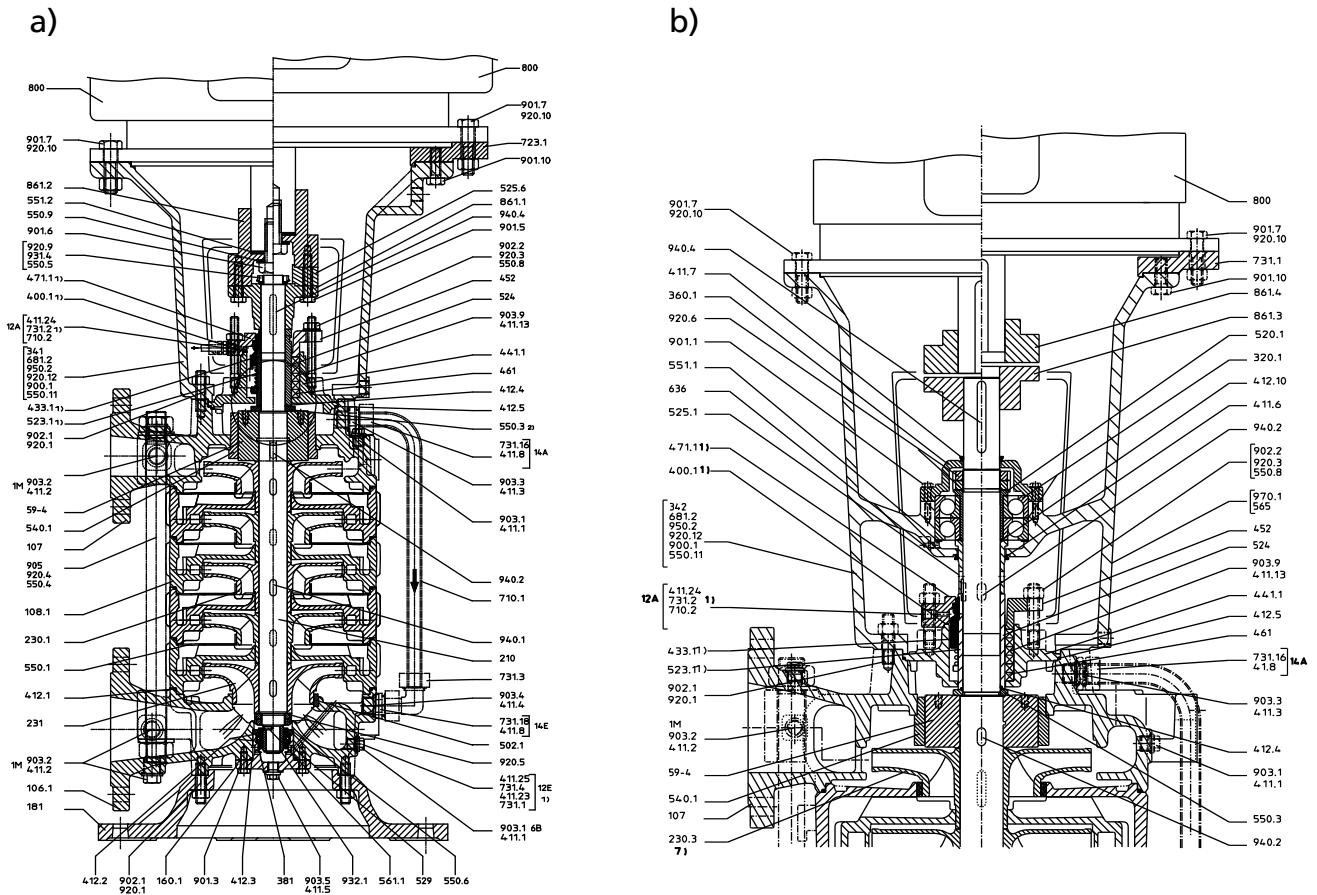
Тип компоновки V - а) Типоразмер 32-65 - б) Типоразмер 100-150
